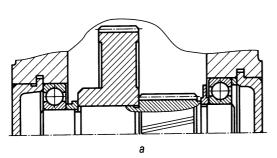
Шестерня цилиндрического зубчатого мотор-редуктора, установленная на валу электродвигателя
